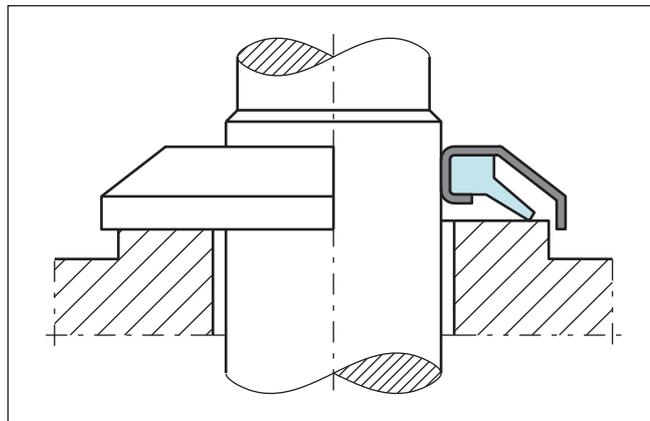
Ausführung der Lauffläche für senkrechte Wellen
